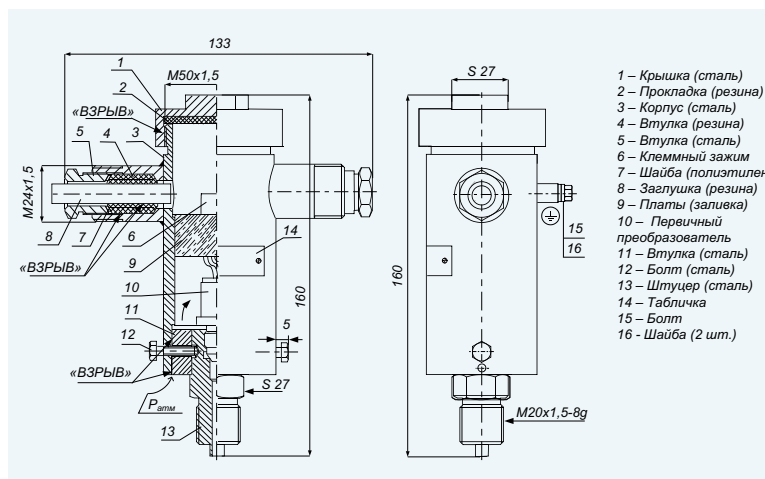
Датчик СЕНС ПД. Габаритный чертеж.
